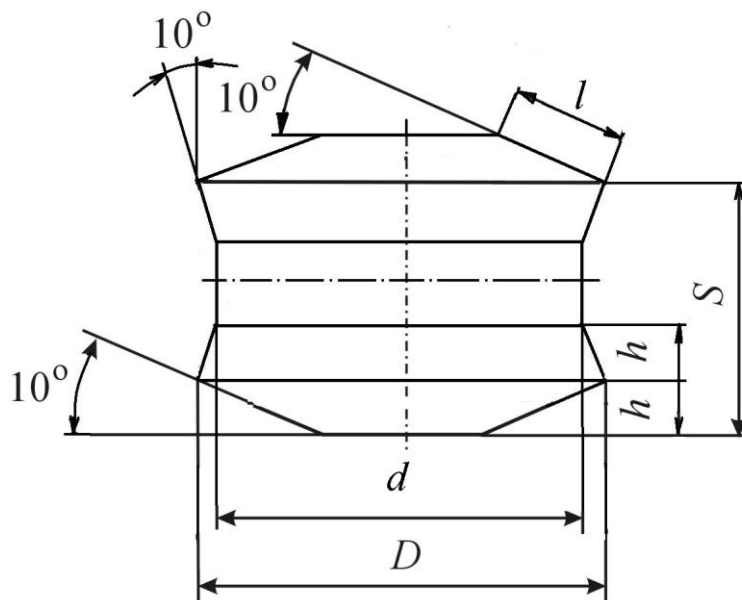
Режущая пластина из ПСТМ двусторонняя коническая
